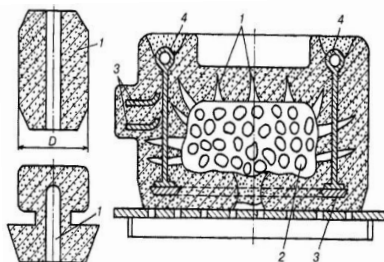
Конструкции стержней: 1 - вентиляционные каналы; 2 - шлак; 3 - каркас; 4 - подъемы
